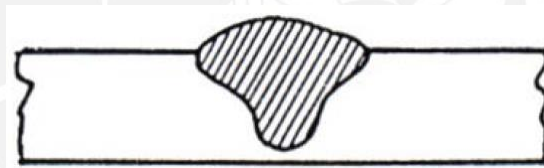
Penetración de la soldadura con electrodos celulósicos
